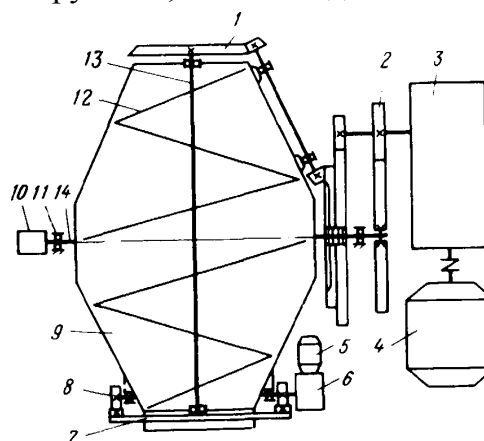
Кинематическая схема смесителя: 1 – открытая зубчатая передача смесительных лопастей; 2 – открытая зубчатая передача барабана; 3, 6 – редукторы; 4, 5 – электродвигатели; 7 – шибер; 8 – открытая зубчатая передача шибера; 9 – барабан; 10 – кольцевой токоприемник; 11 – опорный подшипник; 12 – винтовые лопасти; 13 – вал; 14 – полуось барабана
